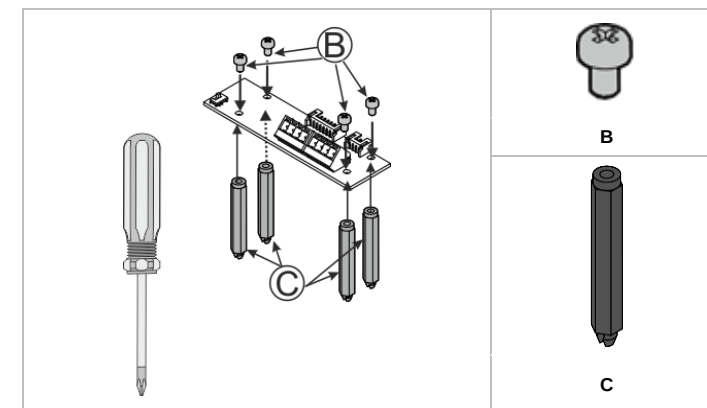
Montage für die TST FUZ2/Assembly for the TST FUZ2/Montage pour le TST FUZ2
